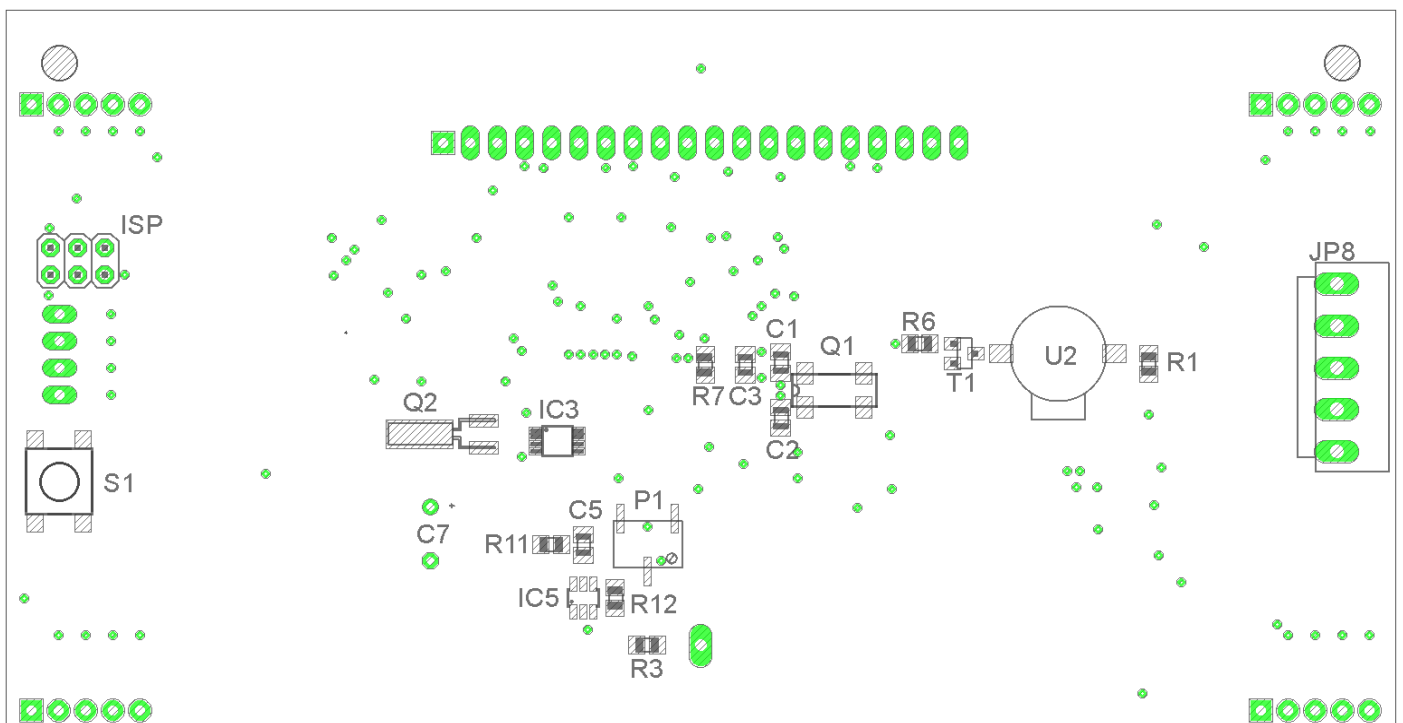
Bestückungsplan BasisPCB Bottom
